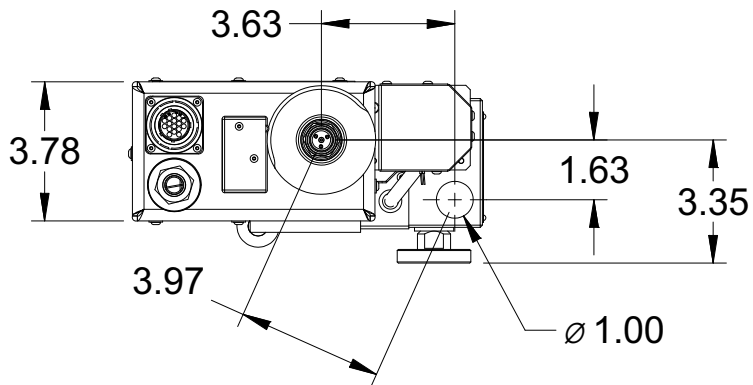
DIMENSIONES DE LA BOREWELDER
